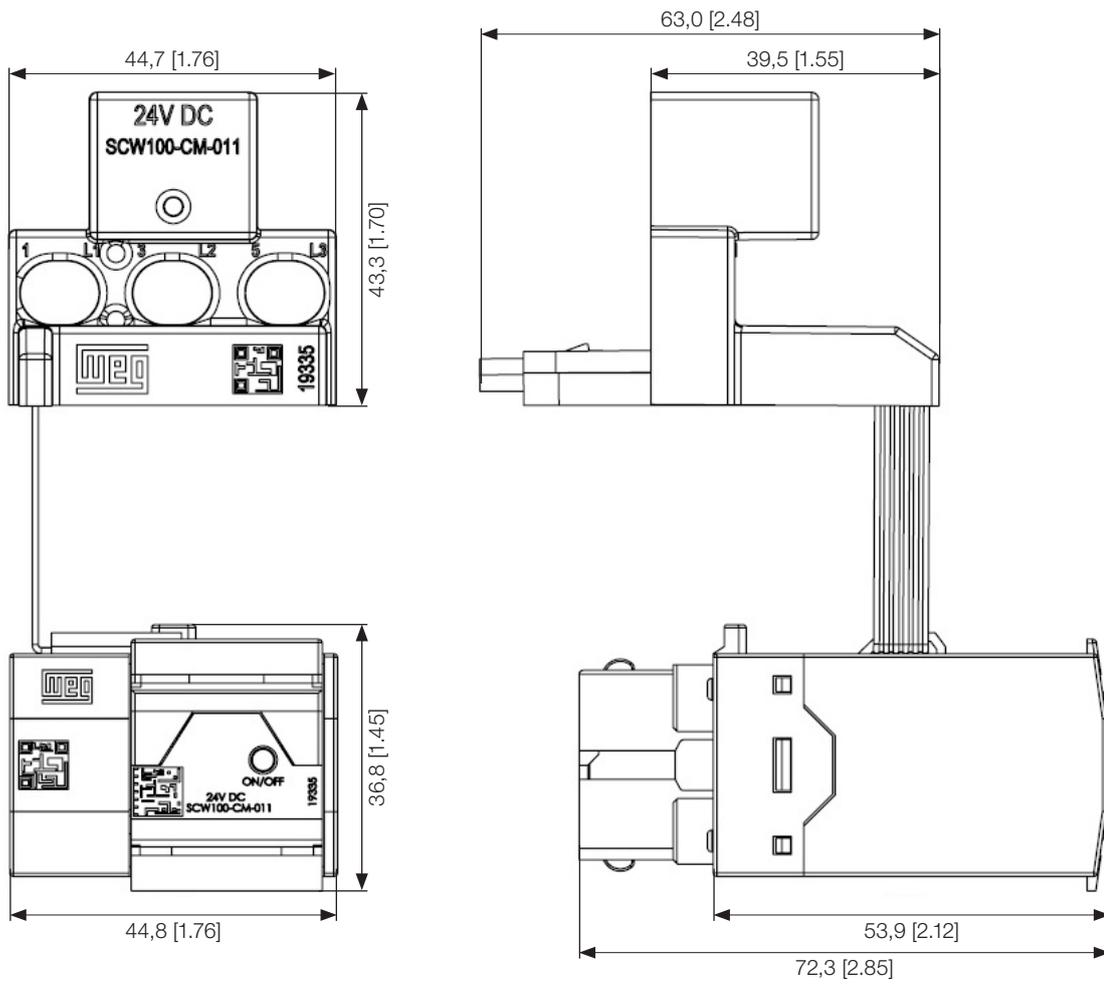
Dimensões do Módulo de Conexão Partida Direta com disjuntor-motor (CM-011) em mm [in]
